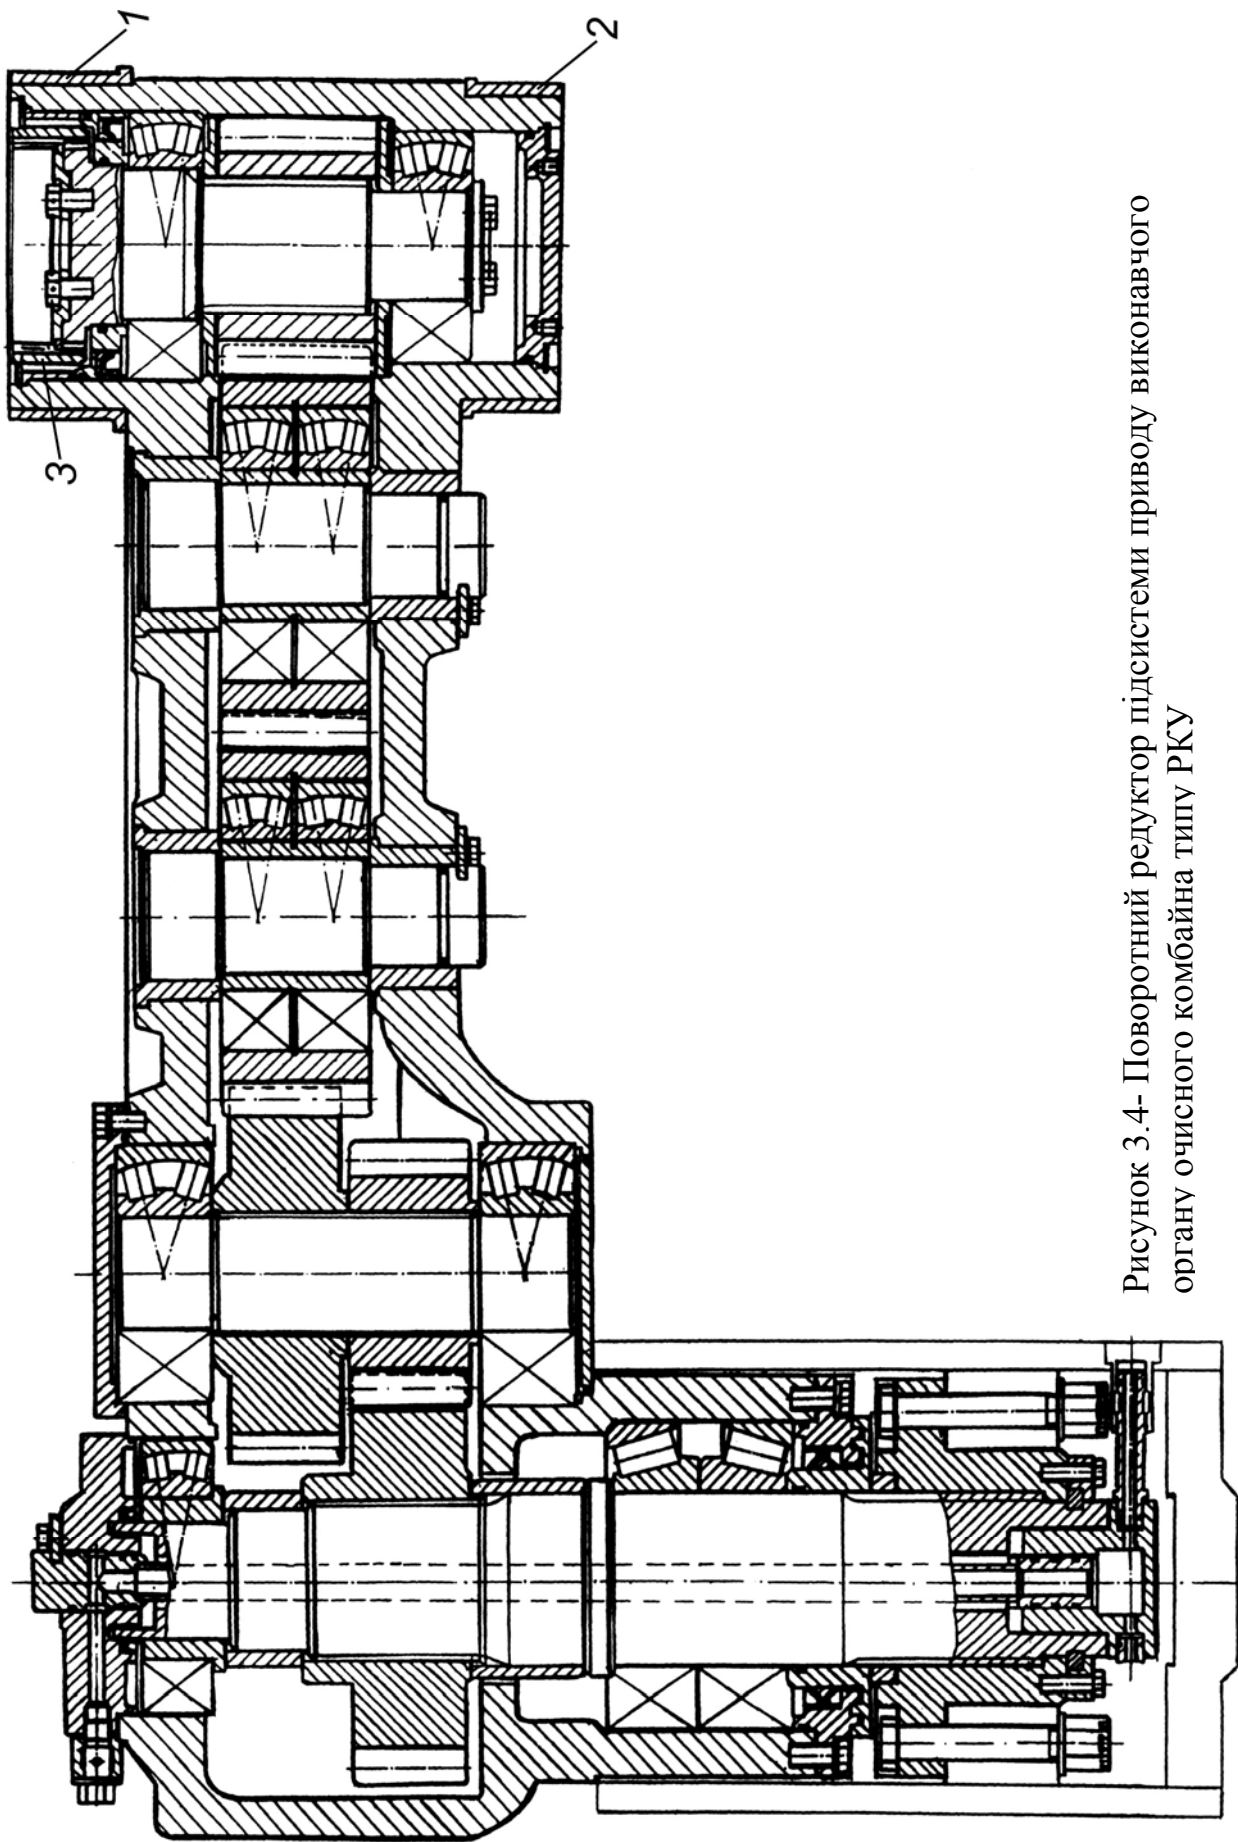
Поворотний редуктор підсистеми приводу виконавчого органу очисного комбайна типу РКУ
